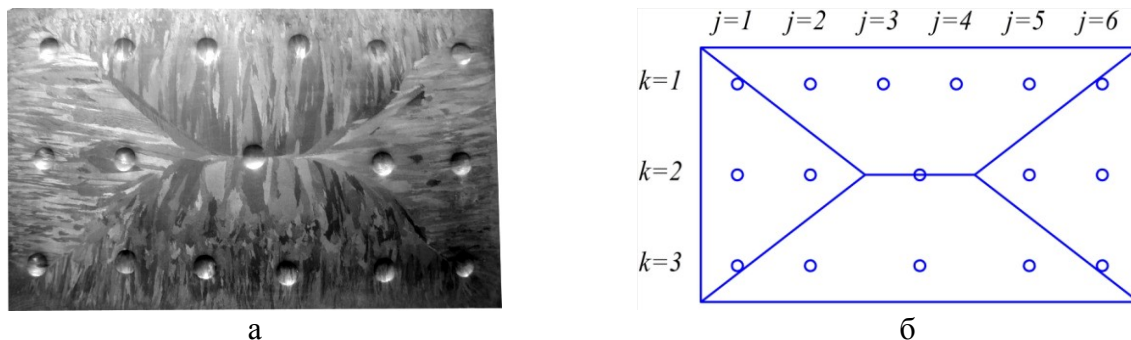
Фотография поперечного темплетта литой заготовки с отпечатками индентора (а) и схема расположения отпечатков (б)
